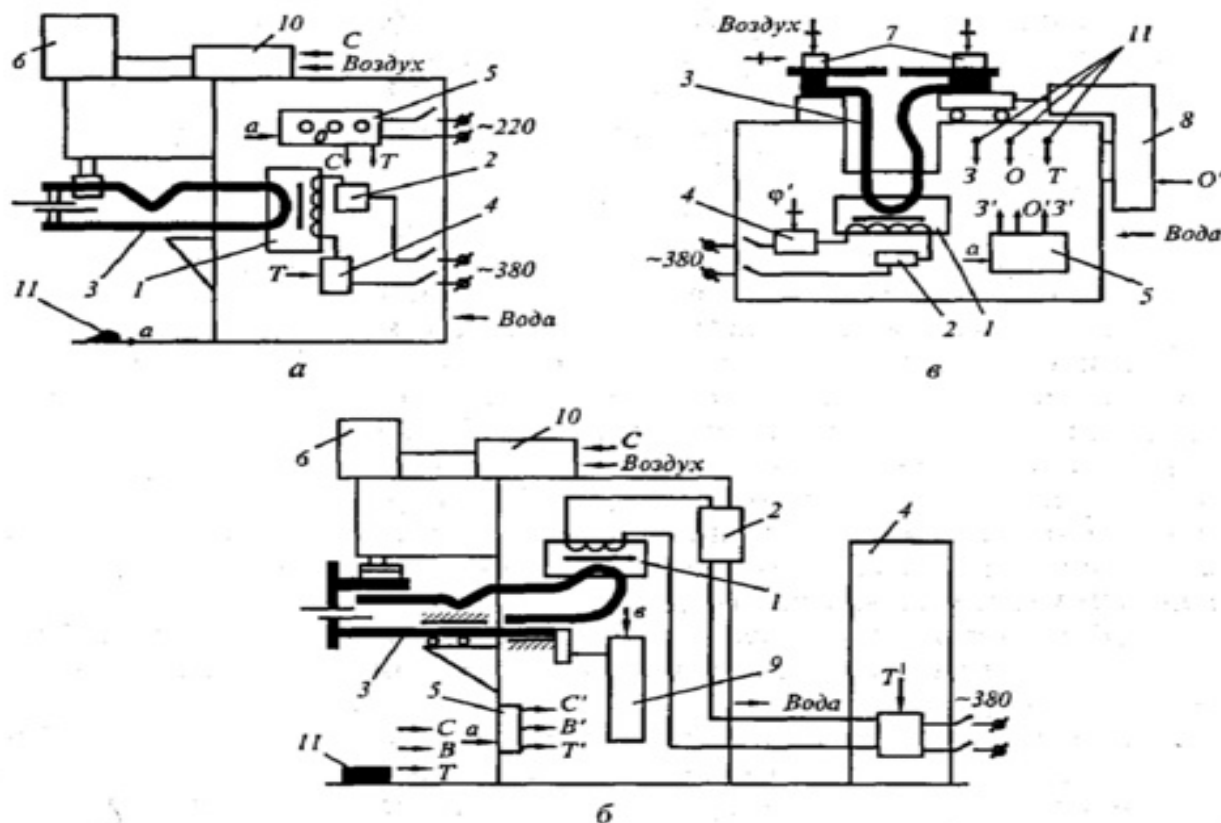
Типовые схемы машин для контактной точечной (а), шовной (б) и стыковой (в) сварки.
